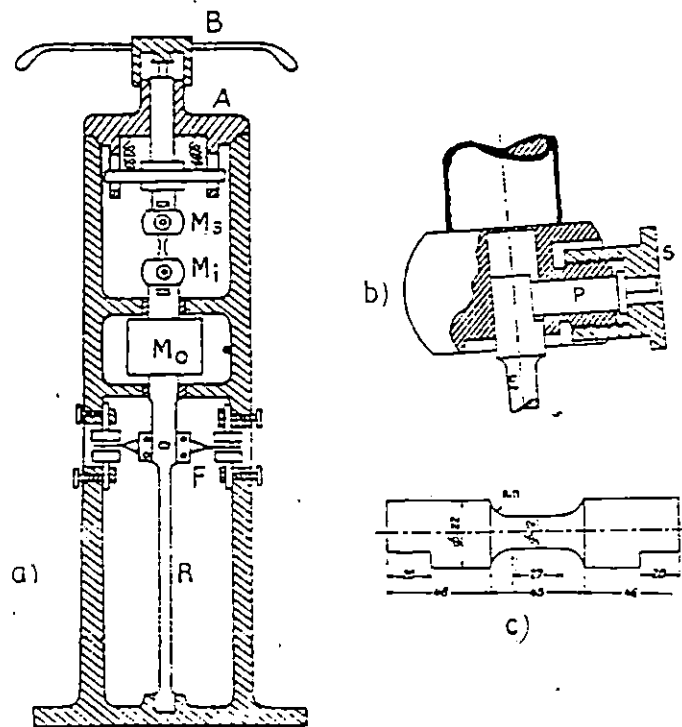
Máquina de Torsión Lausenhausem, a) Esquema de conjunto, b) Montaje de Probeta y c) Probeta.
